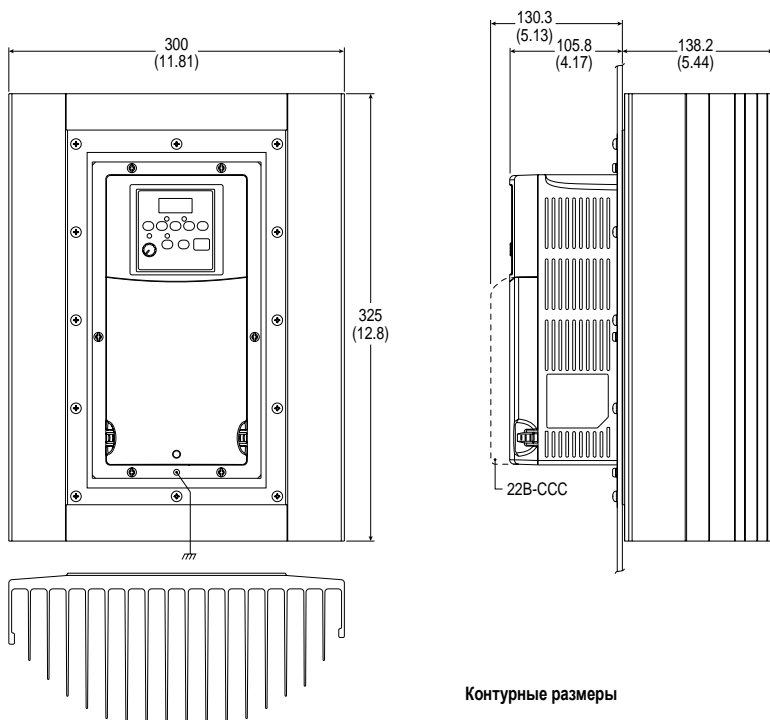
Привод PowerFlex 400 с корпусом С и фланцевым креплением.
